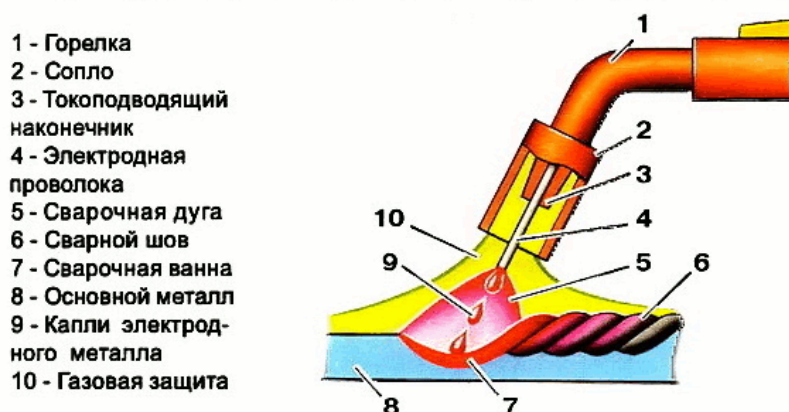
Схема выполнения механизированной сварки в защитных газах проволокой сплошного сечения
